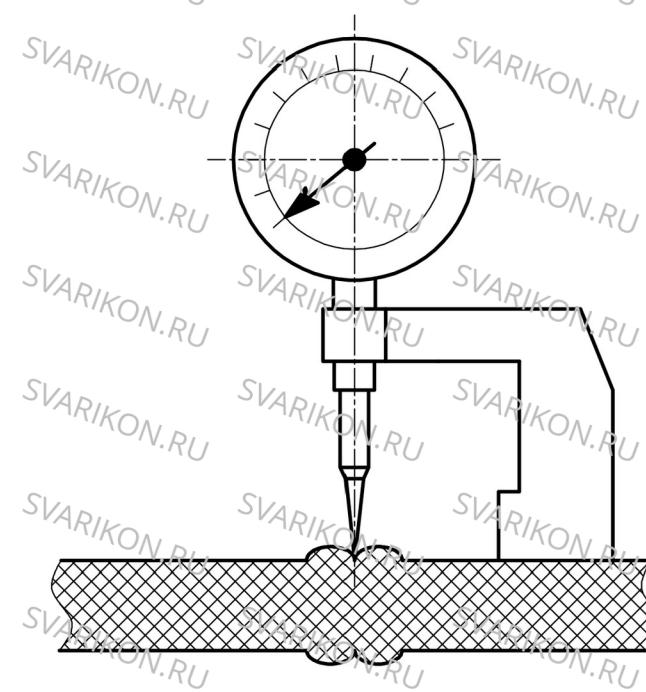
Приспособление для измерения глубины впадины по центру сварного шва.
